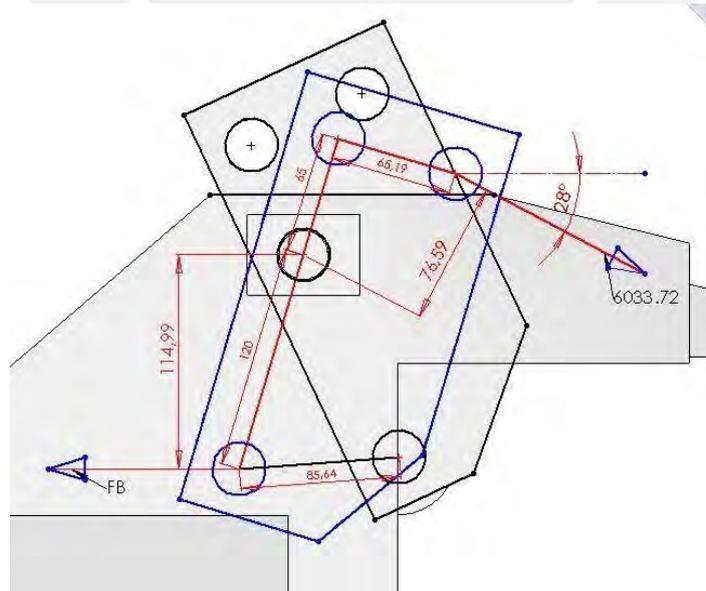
Posiciones de la Placa de Reversión, antes y después del inicio del Levantamiento del arado por el Sistema Hidráulico del Tractor
